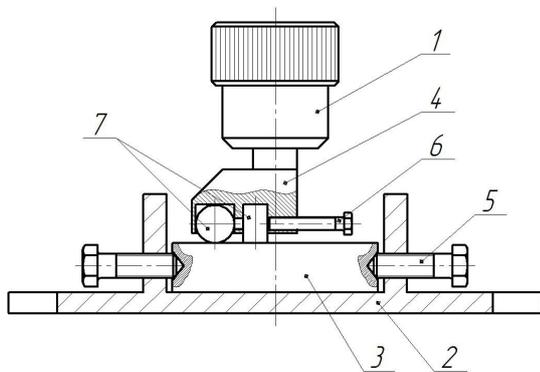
Принципиальная схема трения: 1 — патрон станка; 2 — корпус; 3 — образец неподвижный (шайба); 4 — державка; 5 — крепежный винт корпуса; 6 — винт крепления образцов; 7 — цилиндрический и сферический образец.
